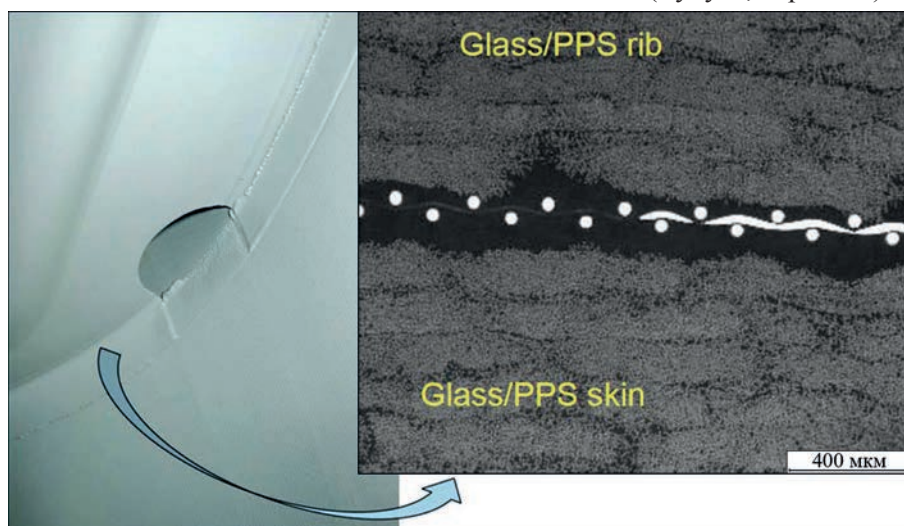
Терморезисторне зварне з'єднання металевою сіткою корпусної деталі та ребра жорсткості, виготовлених із композиту поліфеніленсульфід/скловолокно [8]
